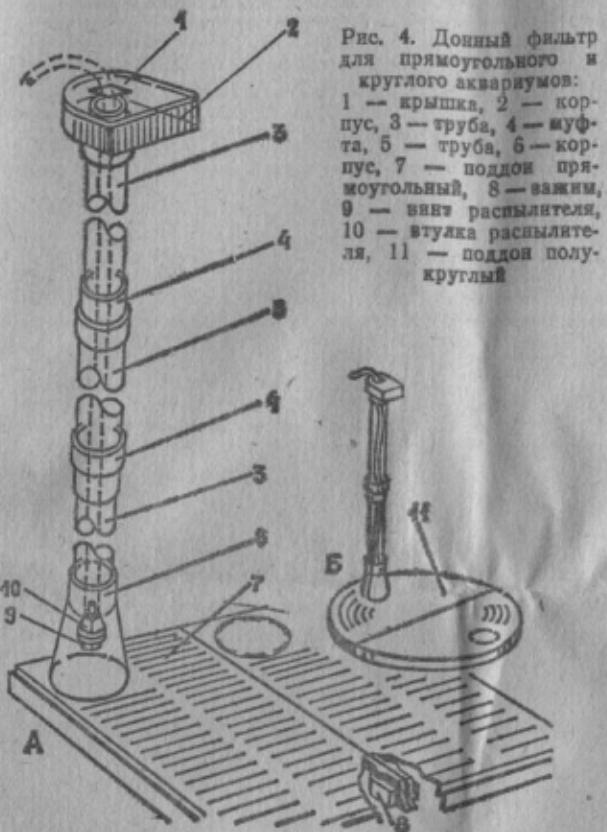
Донный фильтр для прямоугольного и круглого аквариумов:
